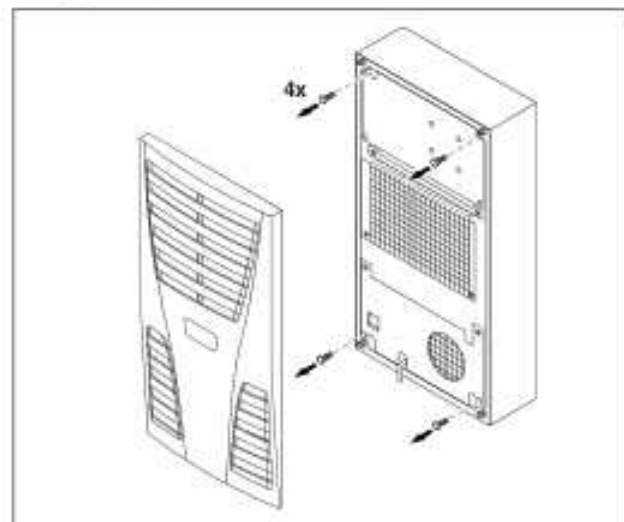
Nur SK 3302.xxx: vier Schrauben entfernen
